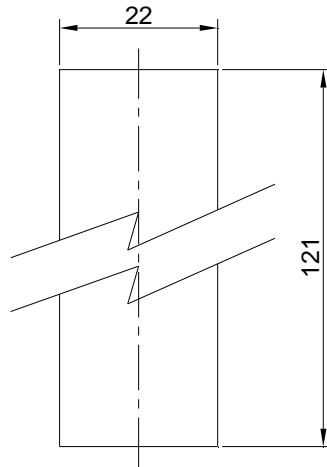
Dimensiones del eje del motorreductor (en mm)
